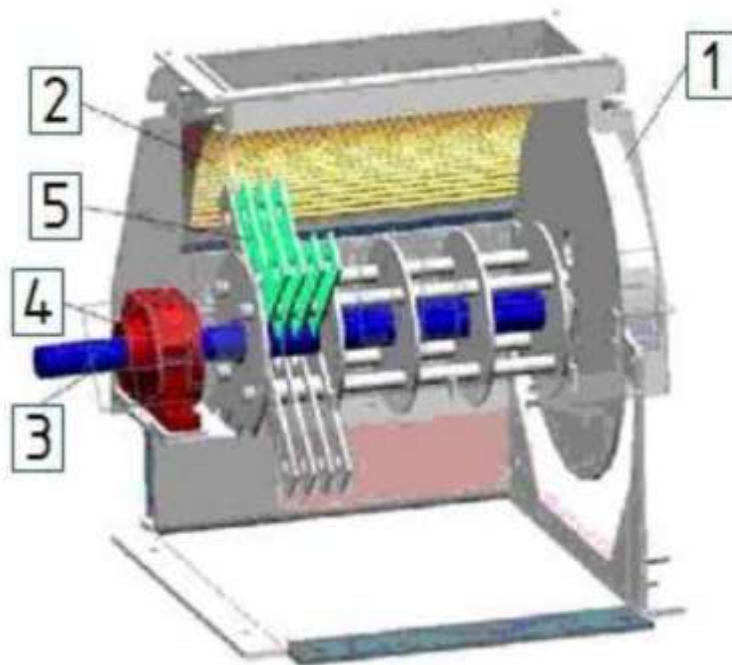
Молотковая дробилка ДМ-5м: 1 - корпус; 2 - дека; 3 - ротор; 4 - подшипниковая опора; 5 - молотки.
